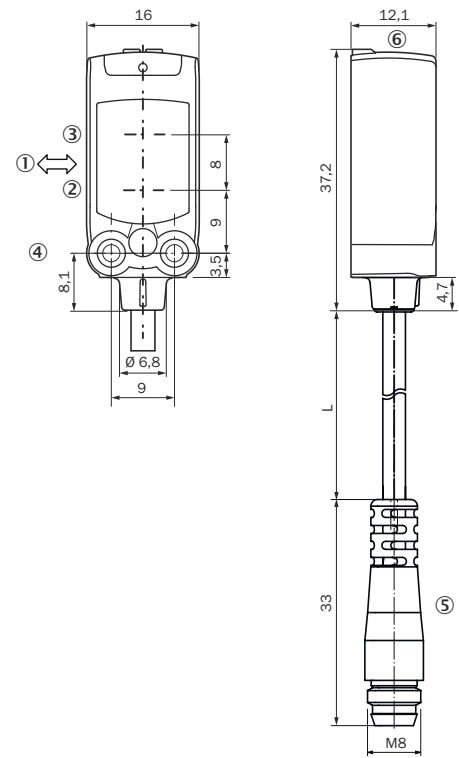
Maßzeichnung, Leitung mit Stecker M8
